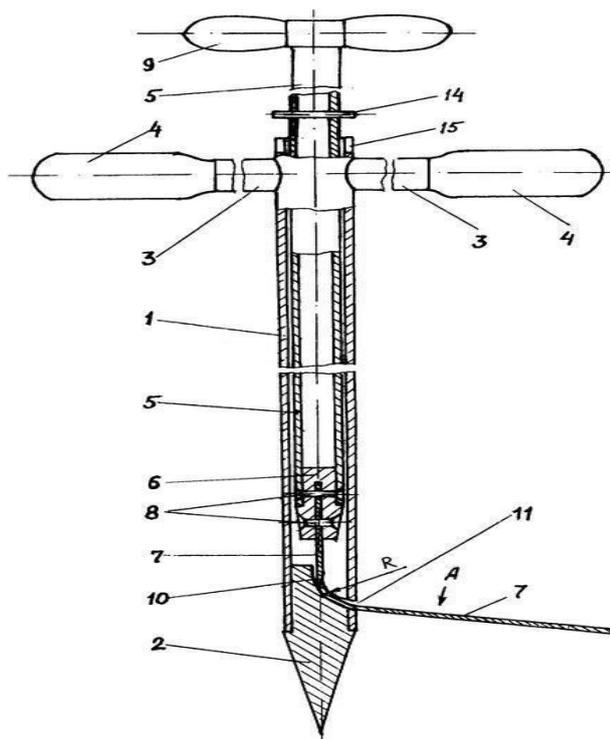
Общий вид устройства для обрезки стержневого
